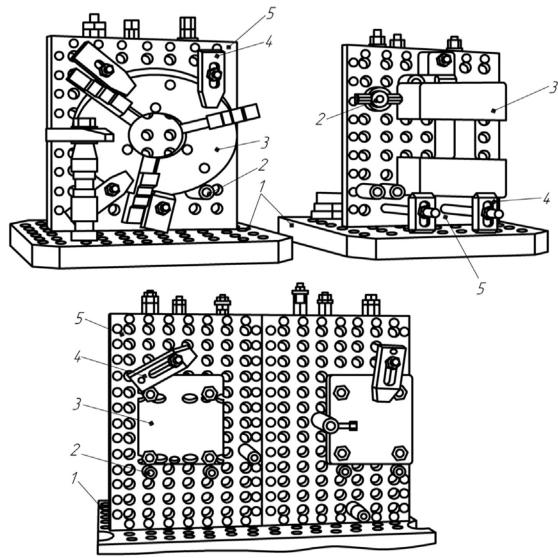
Модульное приспособление для установки корпусной детали: 1 – плита-спутник; 2 – установочный элемент; 3 – заготовка; 4 – зажимной элемент; 5 – угольник
